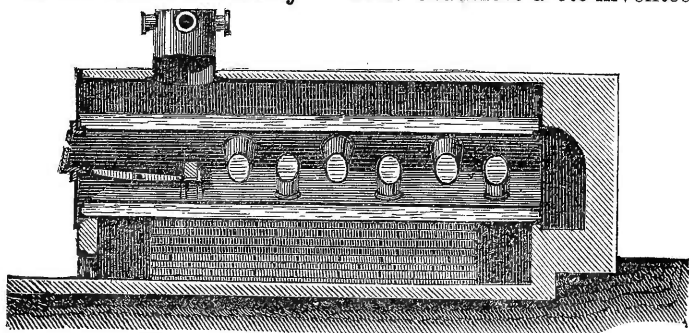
Coupe longitudinale de la chaudière Galloway (Bonnet-Spazin). également en Angleterre; en France, elle est construite par MM. Bonnet-Spazin, à Lyon-Vaise.
